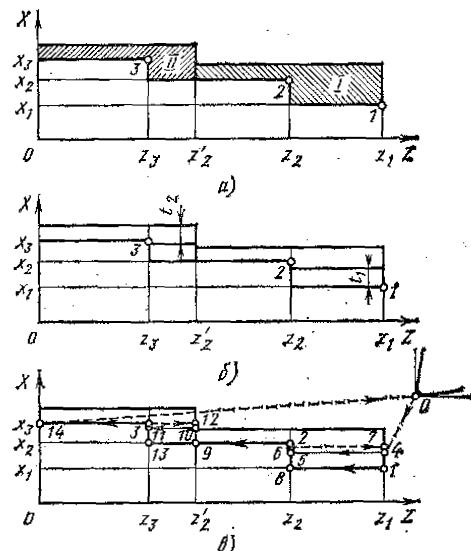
Траектория резца для обработки ступенчатой заготовки
